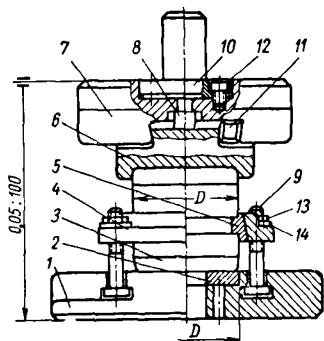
Блок для цилиндрических вставок [4]: 1 — плита нижняя; 2 — прокладка; 3 — вставка цилиндрическая нижняя; 4 — обойма; 5 — кольцо разрезное; 6 — вставка цилиндрическая верхняя; 7 — плита верхняя; 8 — шпонка; 9 — болт; 10 — хвостовик с фланцем; 11 — клин верхний; 12 — винт; 13 — гайка; 14 — шайба
